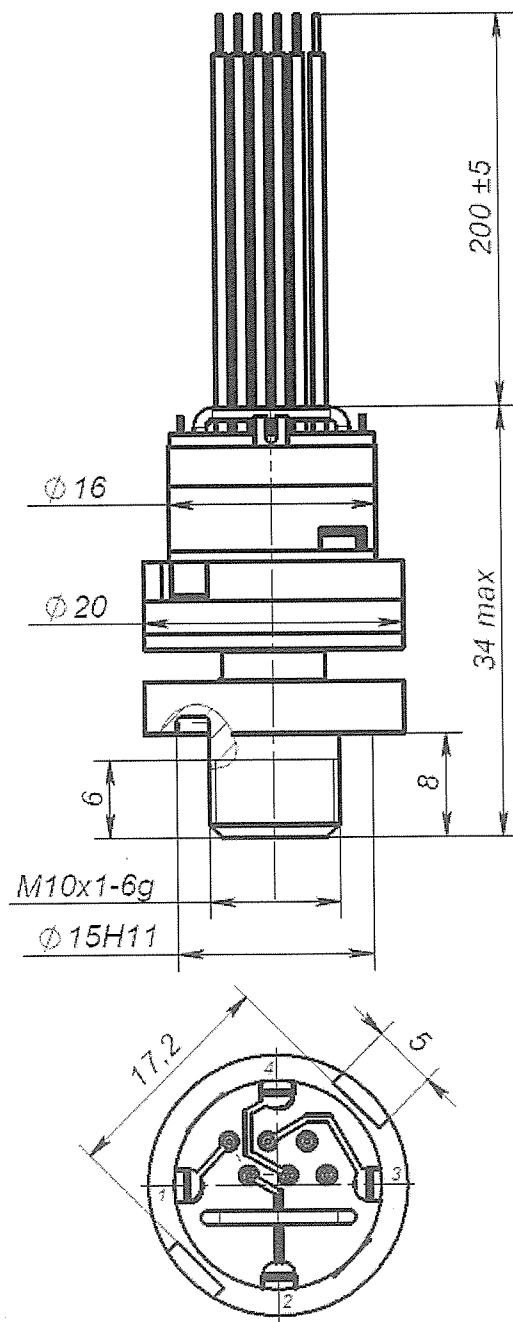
Габаритные и присоединительные размеры тензопреобразователя Д0,1ПМТ-2
